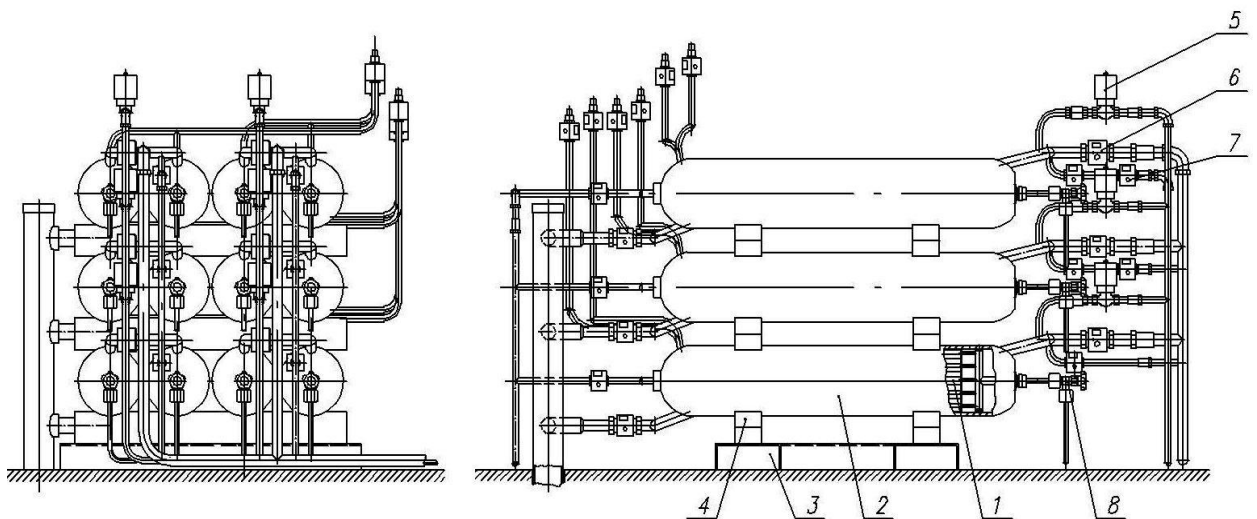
Металлогидридный компрессор ТСК1–3,5/150
